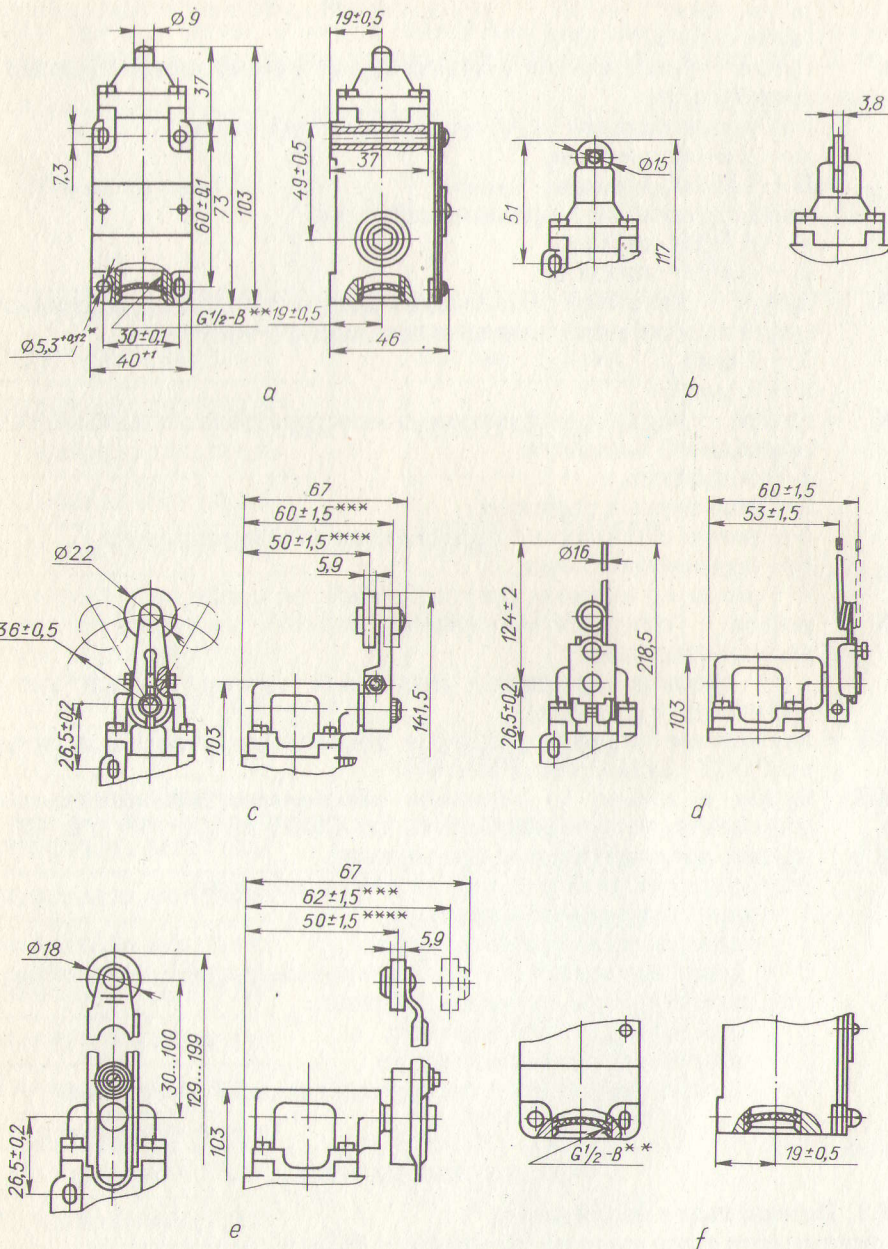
Габаритные, установочные и присоединительные размеры выключателей:
